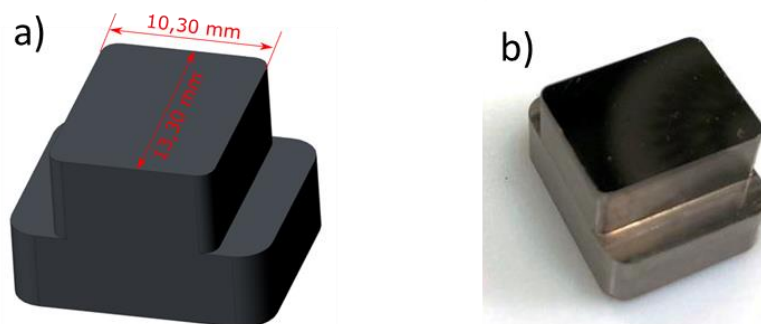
a) CAD-Design des Werkzeugeinsatzes mit Abmessungen, b) Werkzeugeinsatz vor dem Ionenstrahlschreiben
